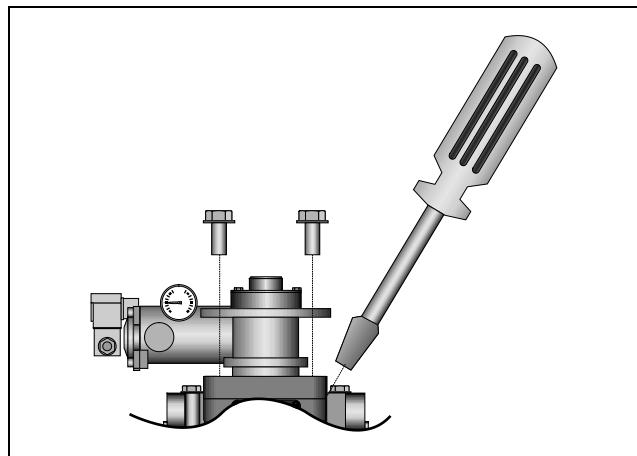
Desserrer et retirer les vis hexagonales du couvercle de filtre.
